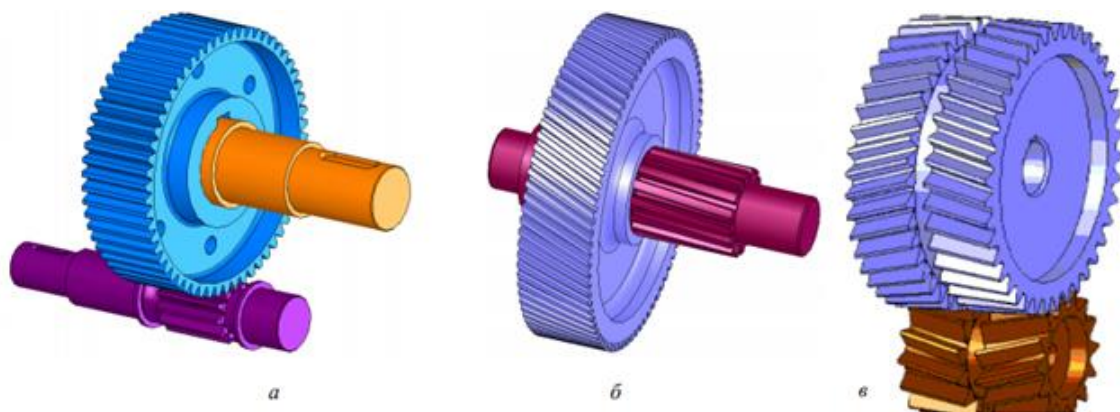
Классификация зубчатых передач по расположению зубьев относительно образующей обода колеса
